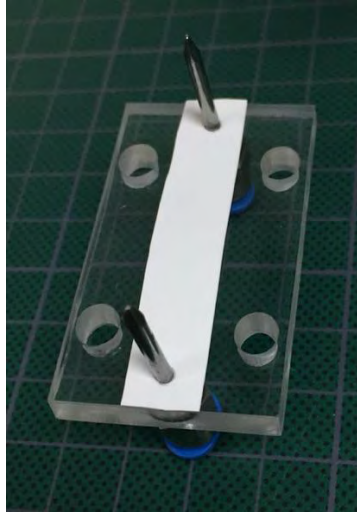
Utilización de guías sobre la placa final para ensamblar las mili-PEMFC por separado.
